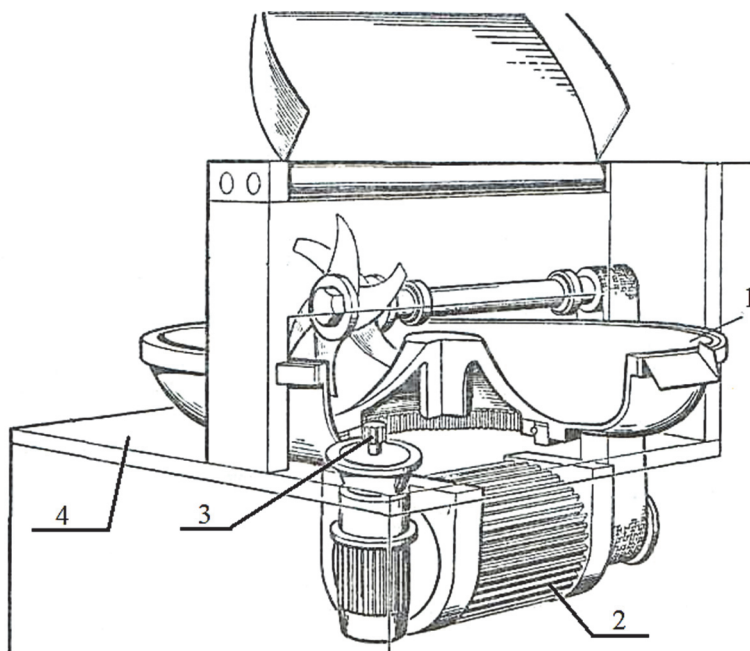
Прототип чаши куттера: 1 – чаша; 2 – привод; 3 – зубчатая передача; 4 – станина
